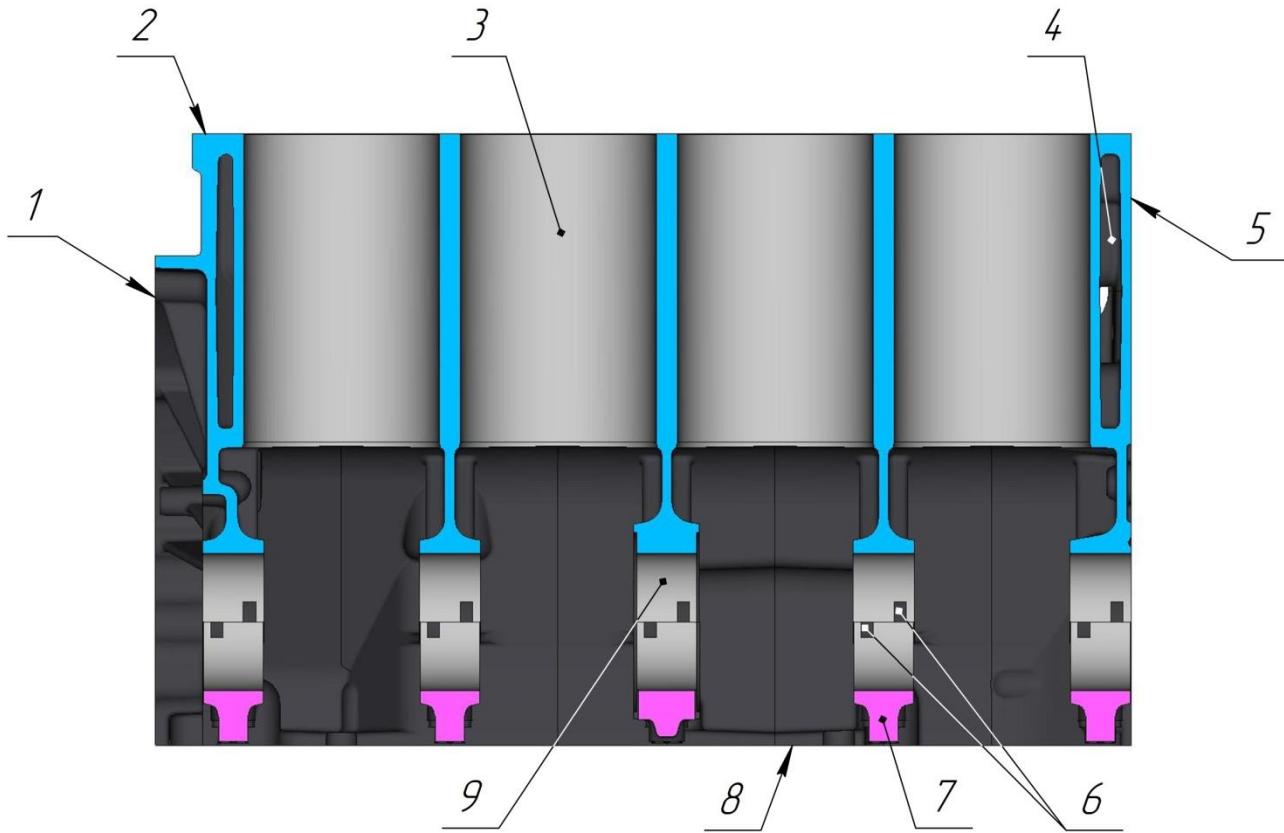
Блок цилиндров. Продольный разрез по оси цилиндров:
